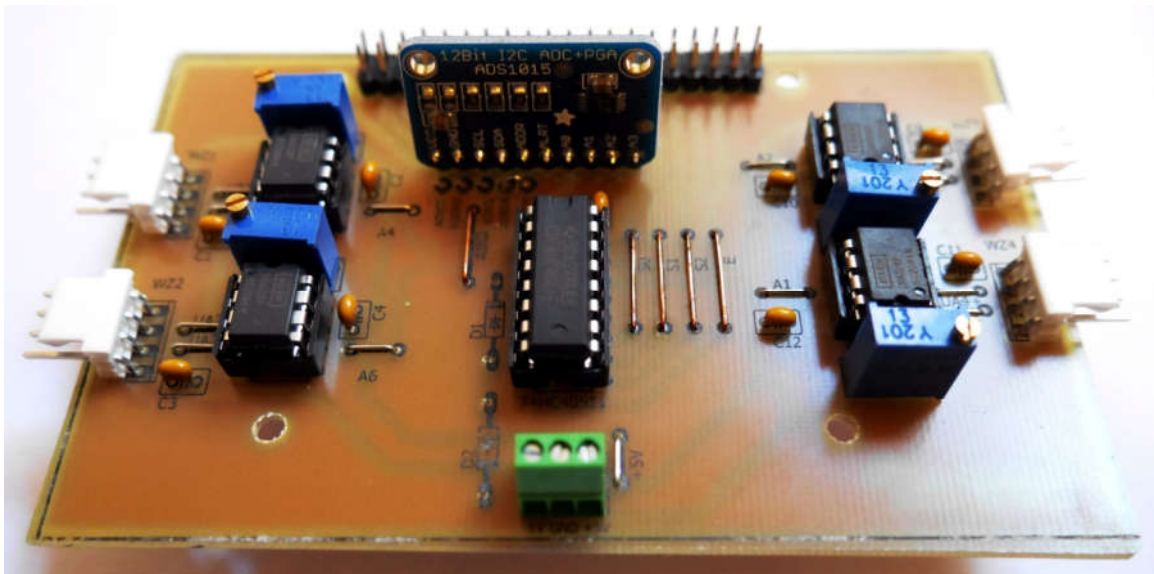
Bestückter Prototyp der Gewichtsmessplatine
